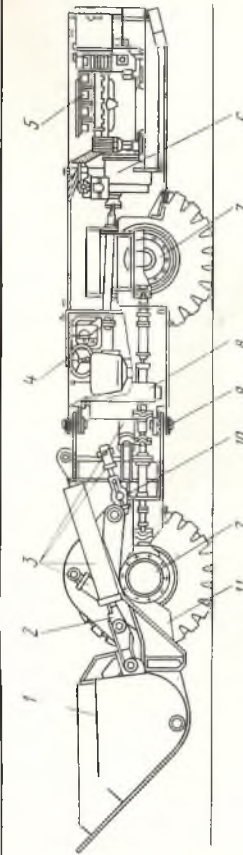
Ковшовая погрузочно-доставочная машина типа G-ST: 1 - ковш; 2 - стрела; 3 - гидроцилиндр; 4 - тяга; 5 - двигатель; 6 - гидротрансформатор; 7 - мост; 8 - коробка передач; 9 - шарнир; 10 - каток; 11 - рычаг
